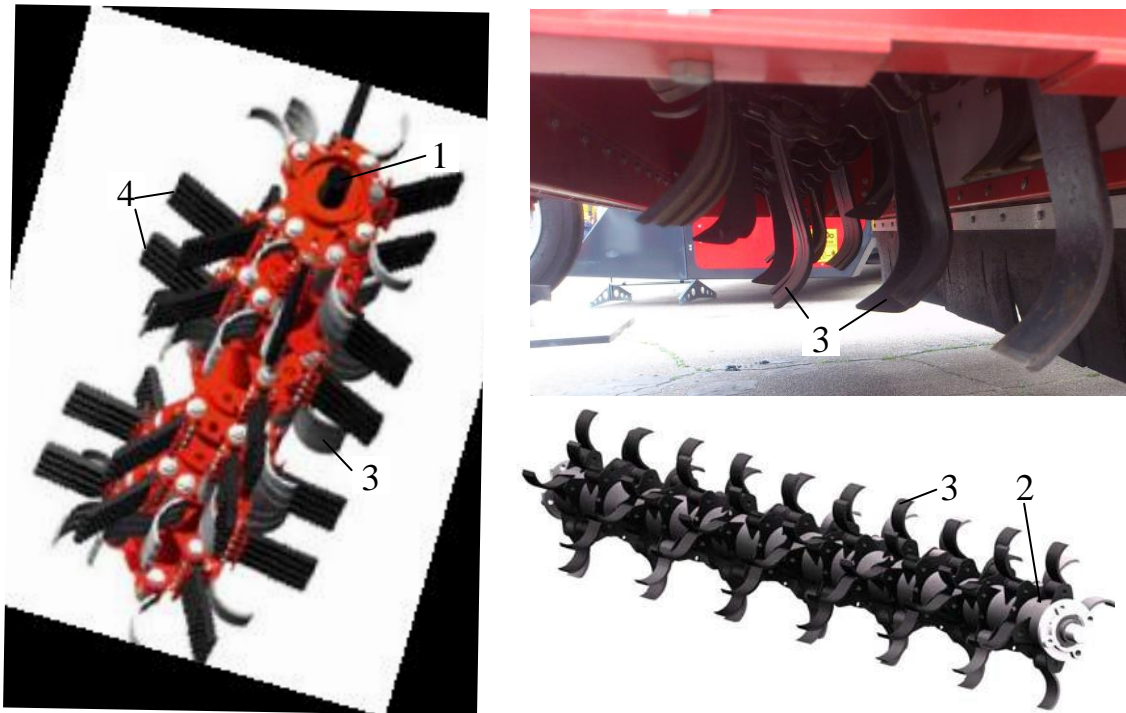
Загальний вигляд роторного гичкоріза: 1 – вал; 2 – барабан;
